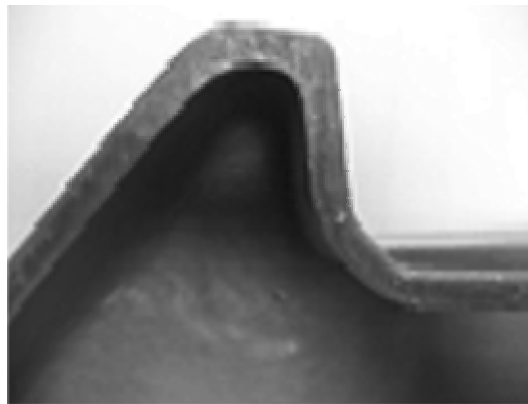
Muestra del espesor de pared de una pieza rotomoldeada.
